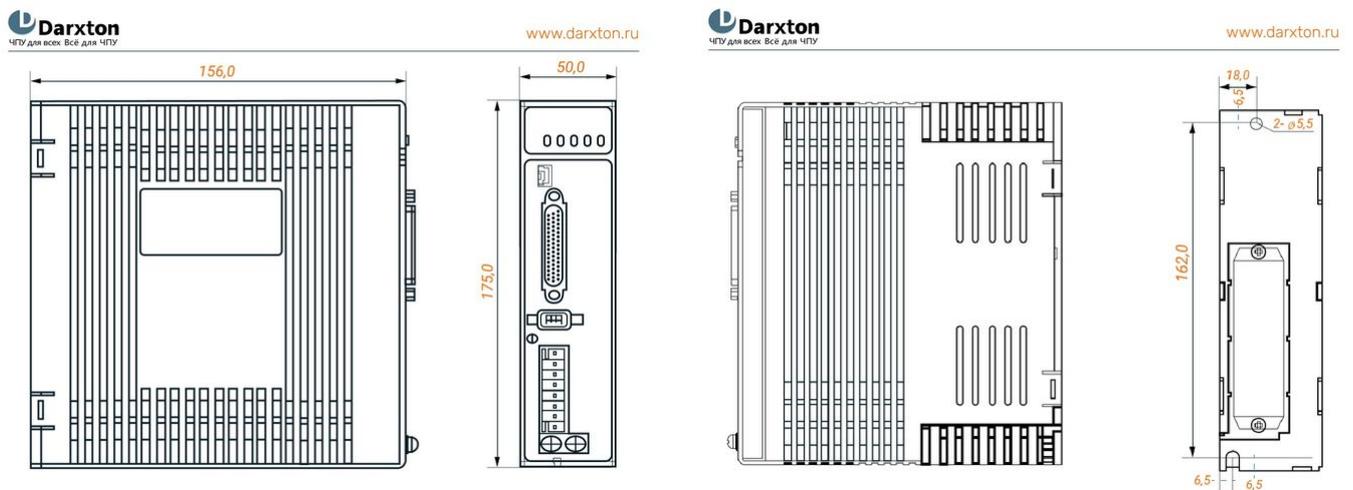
Габаритные размеры драйверов ELP-RS750Z и ELP-RS1000Z
